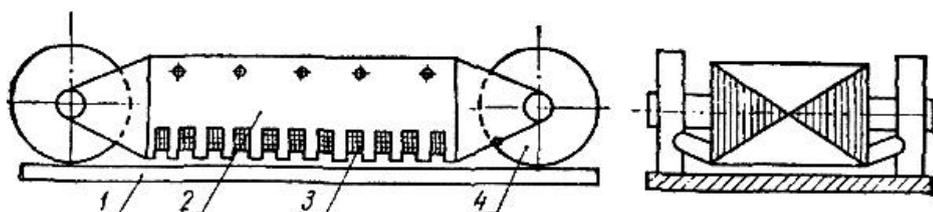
Одноиндукторный линейный двигатель с одной обмоткой и одной реактивной полосой
